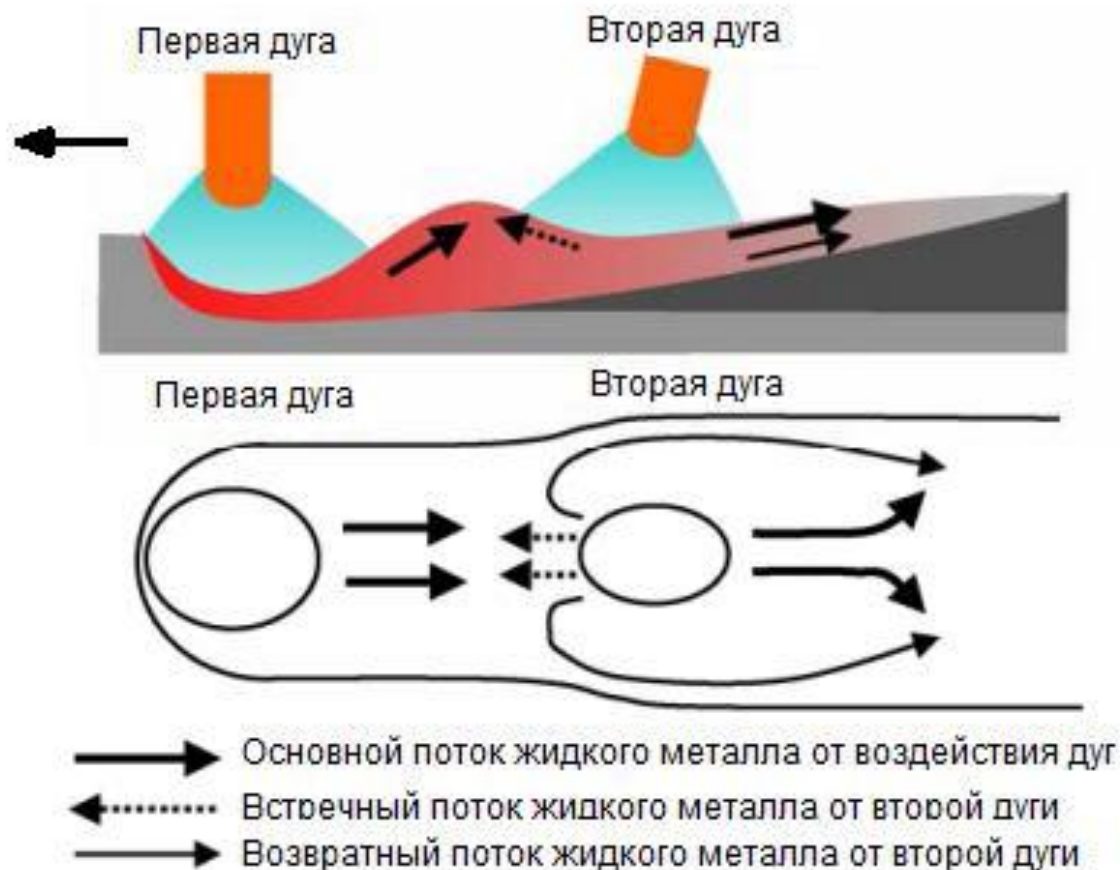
Формирование сварочной ванны в процессе двухдуговой сварки согласно [57]
